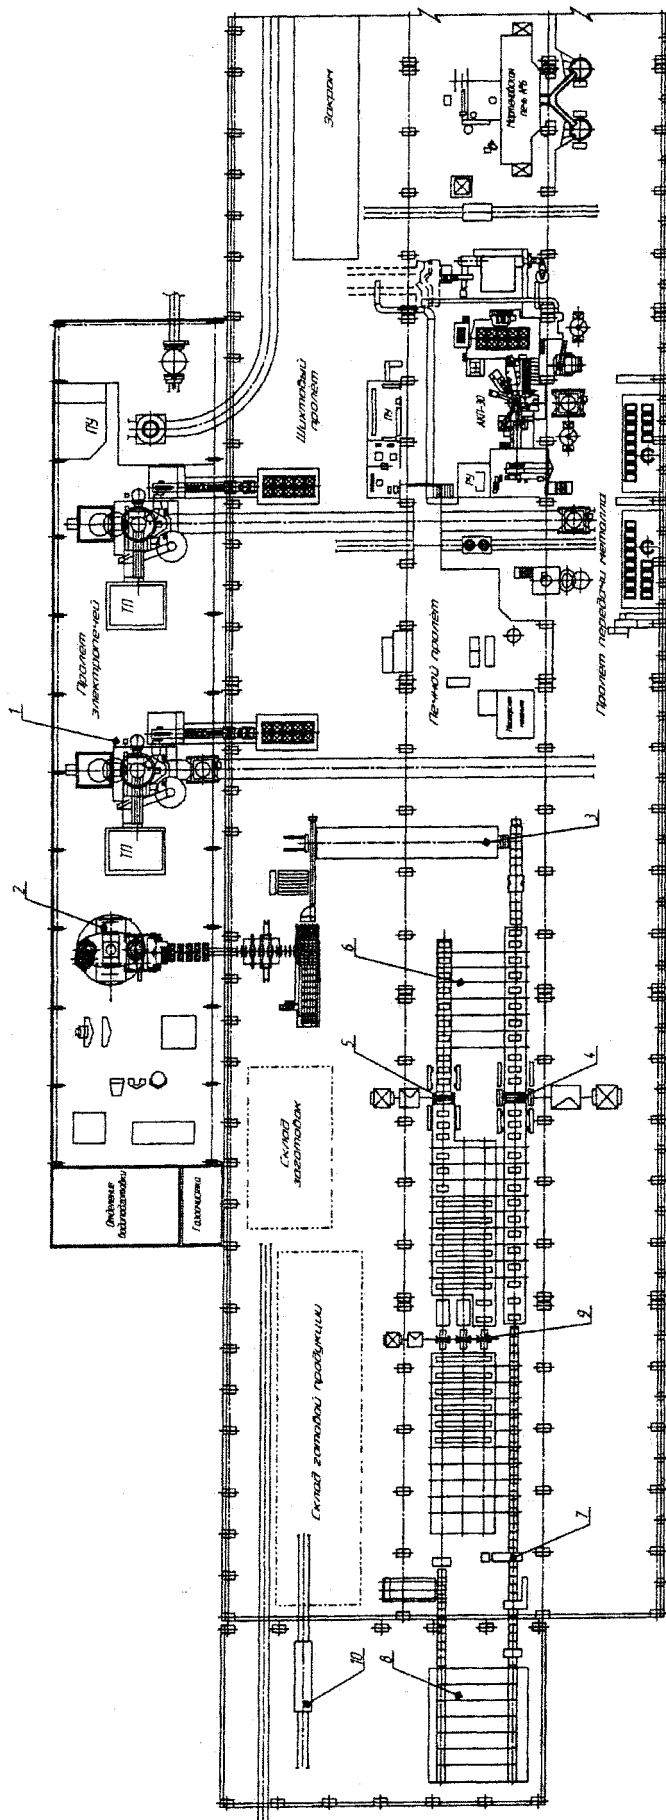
Литейно-прокатный комплекс «МНЛЗ» — крупносортно-среднесортный стан 900/600/500»: 1 — участок сталеплавильных печей; 2 — МНЛЗ; 3 — нагревательная печь; 4 — линия реверсивной клетки дуо 900; 5 — линия реверсивной клетки дуо 600; 6 — шлеперное устройство; 7 — пила горячей резки; 8 — холодильник; 9 — линия клетей трио 500; 10 — передаточная тележка
